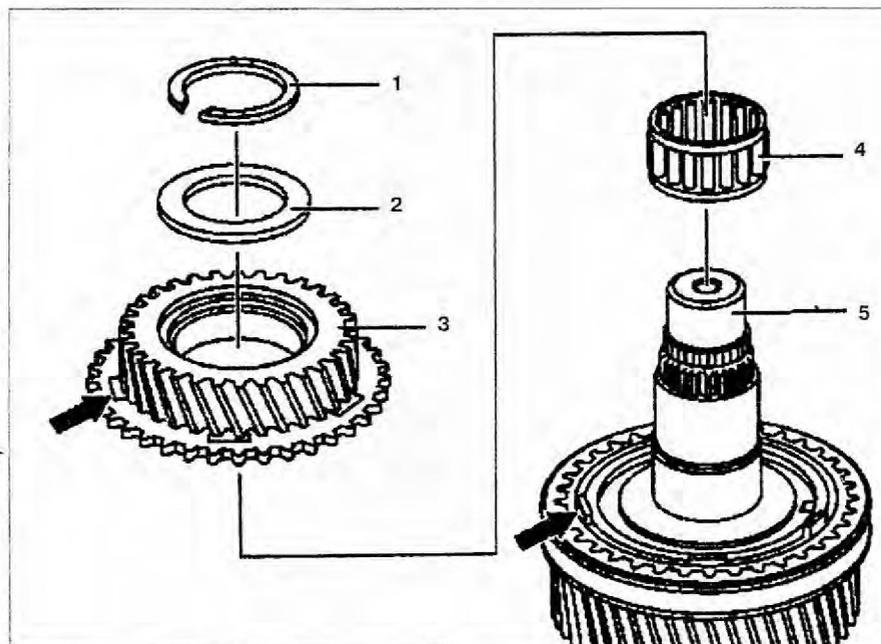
Снятие и установка шестерни 4-й передачи:
